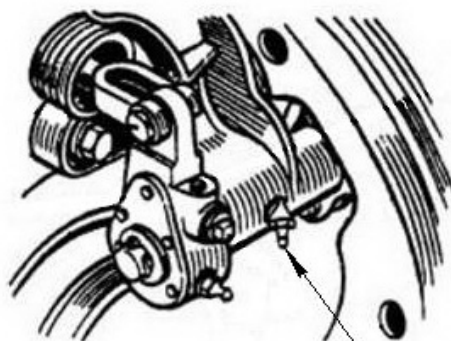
Смазка оси разжимного кулака тормозного механизма
